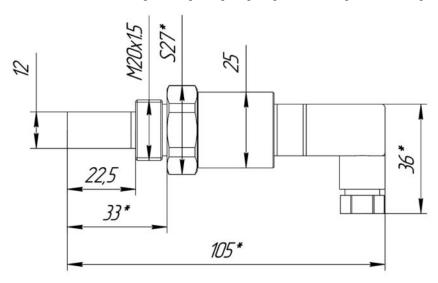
Установочные и габаритные размеры преобразователя ДТР-3-Т20-М.
